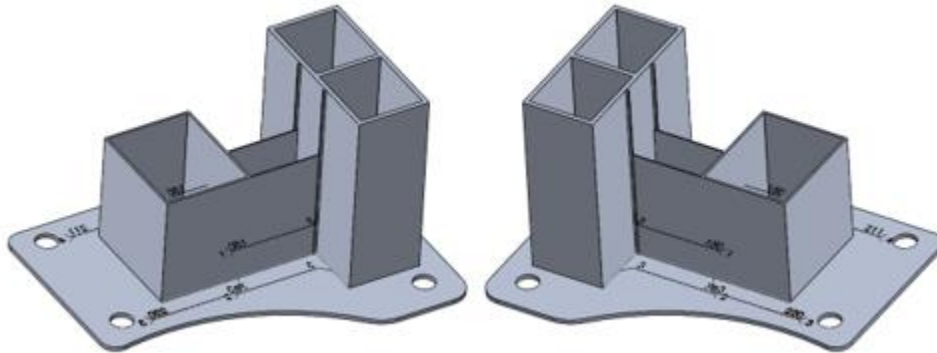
Ensamble de la estación de soldadura 1.
